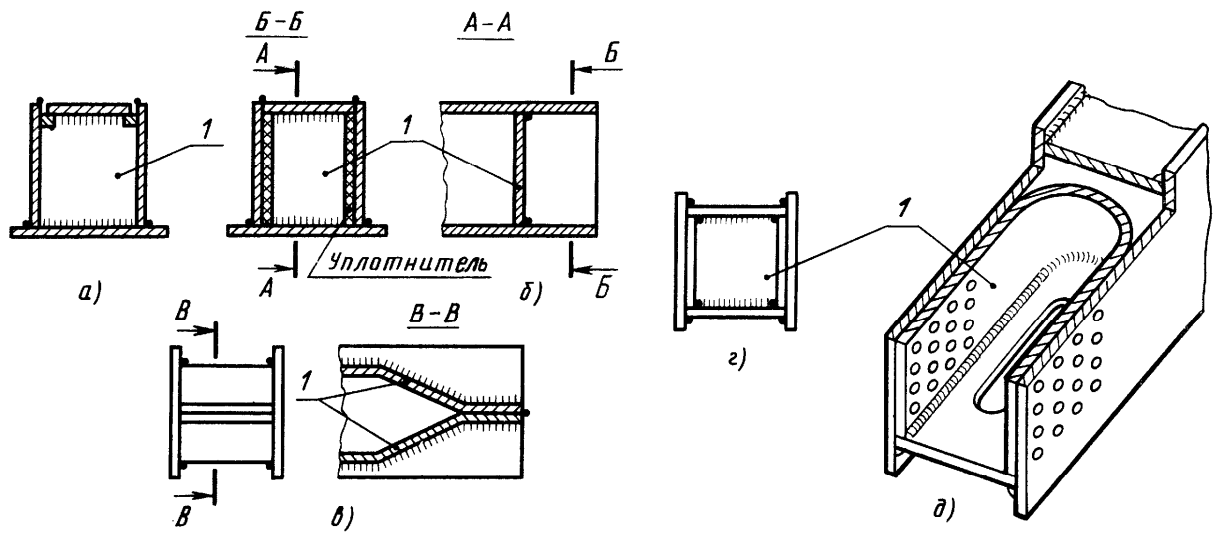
Поперечные сечения сварных коробчатых элементов
